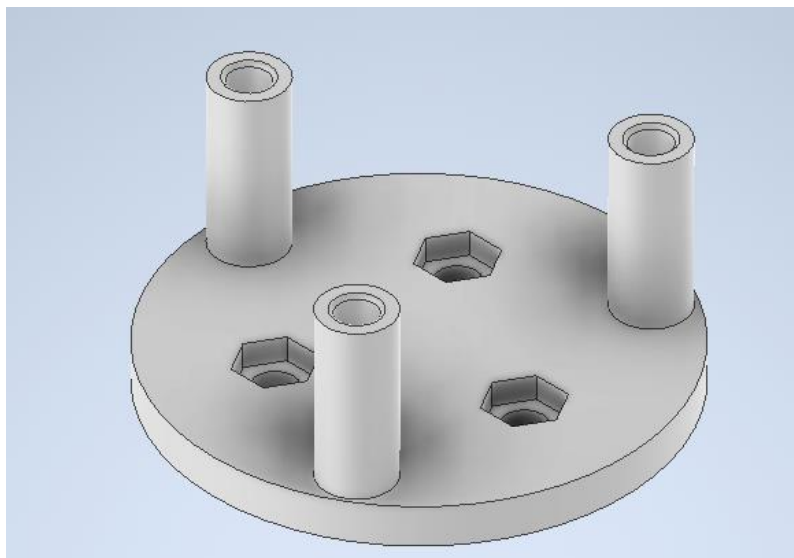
Деталь “Кріплення поворотного столику”
